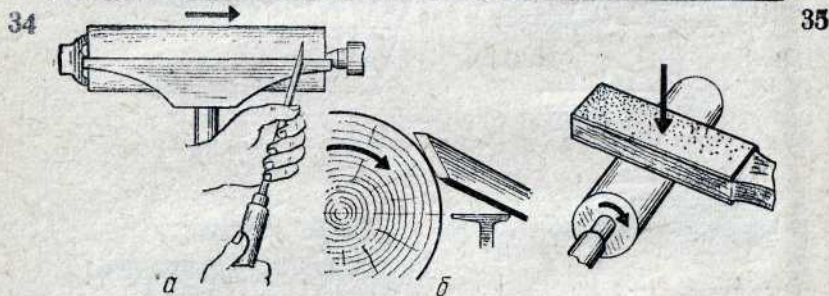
Чистовое обтачивание заготовки: а — хватка стамески; б — положение стамески (увеличено).
